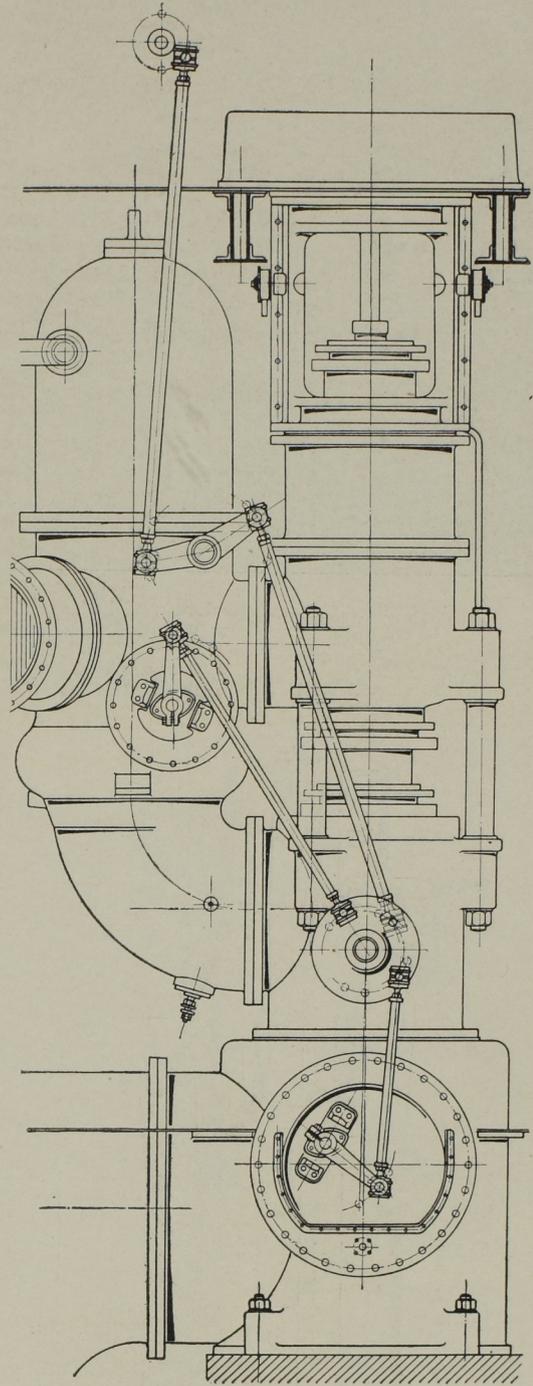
Steuerung einer Pumpe. Masst. 1:50.
